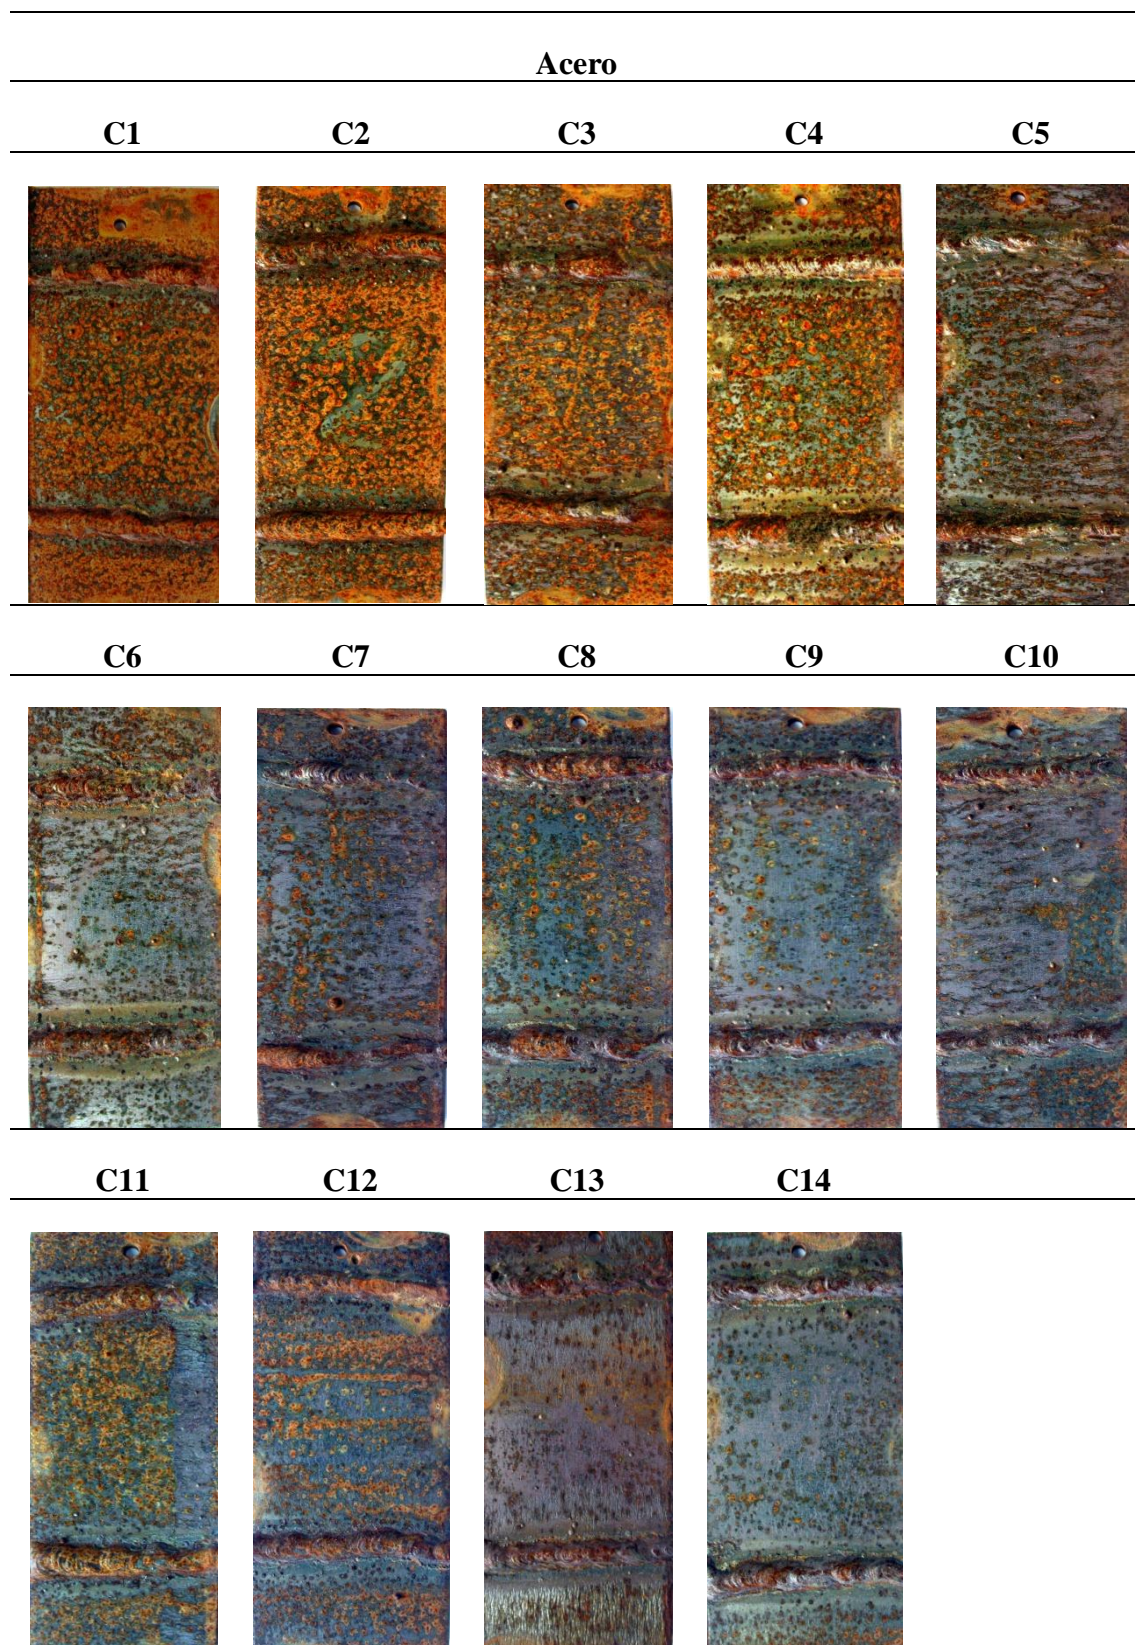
Aspecto que presentaban las probetas con uniones soldadas después de un año de exposición en la atmósfera rural de El Pardo.
